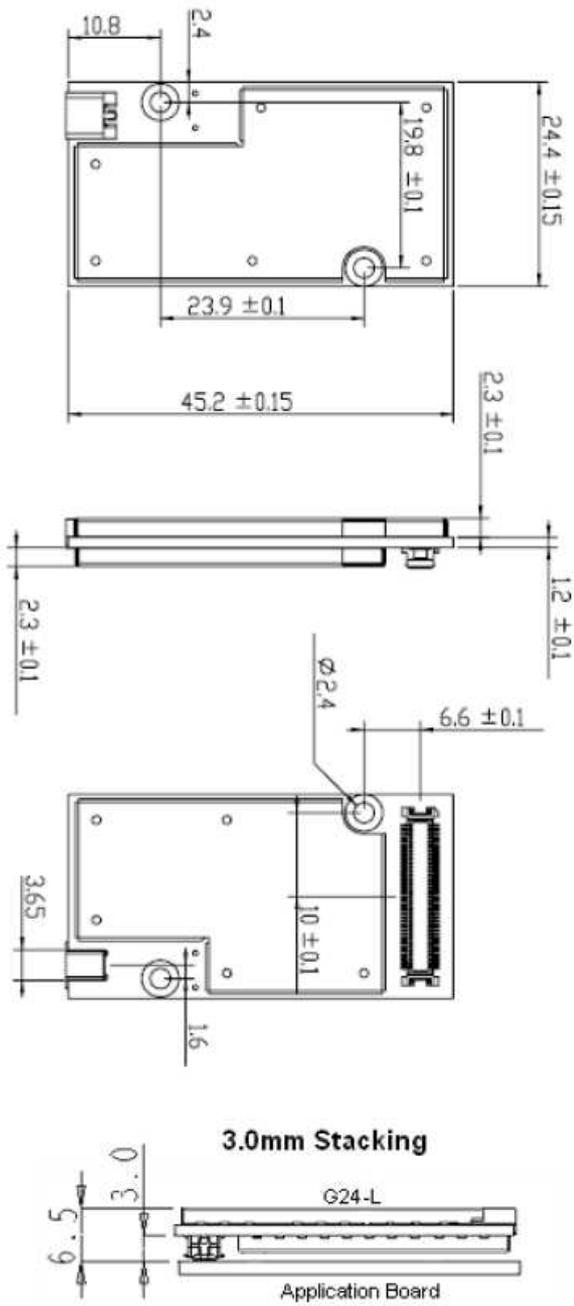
Dimensiones físicas de los Módulos Motorola G24 y G24-L.
